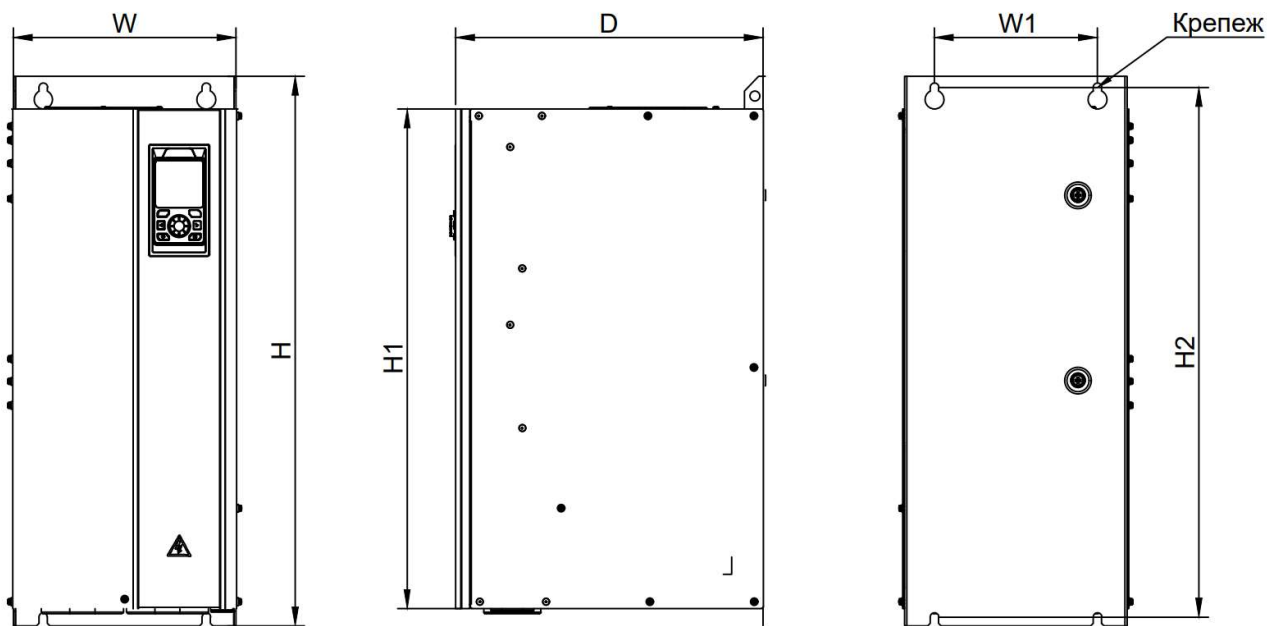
Чертеж преобразователя частоты типоразмеров М6-М11
